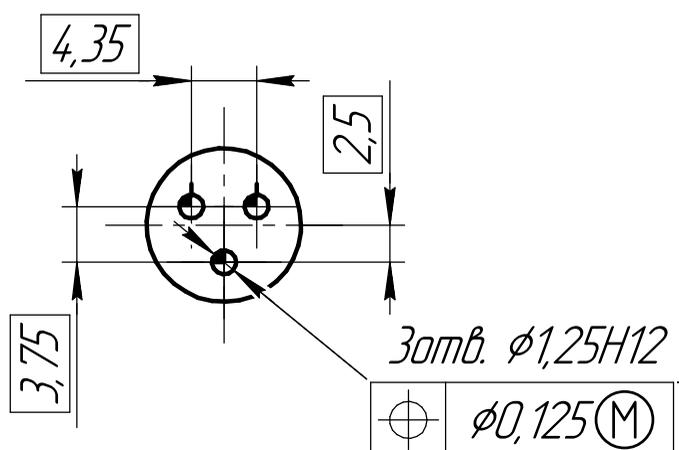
Разметка отверстий для ОСН-25-3/14...П-...
